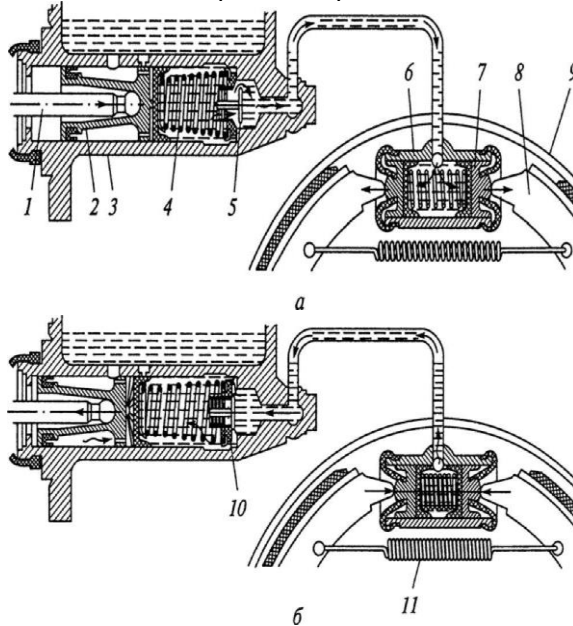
Схема роботи гідравлічного гальмівного приводу: *а* - гальмування; *б* - розгальмування; 1 - штовхач; 2,7 - поршні; 3,6 - циліндри; 4,11 - пружини; 5,10 - клапани; 8 - колодка; 9 - гальмівний барабан.
